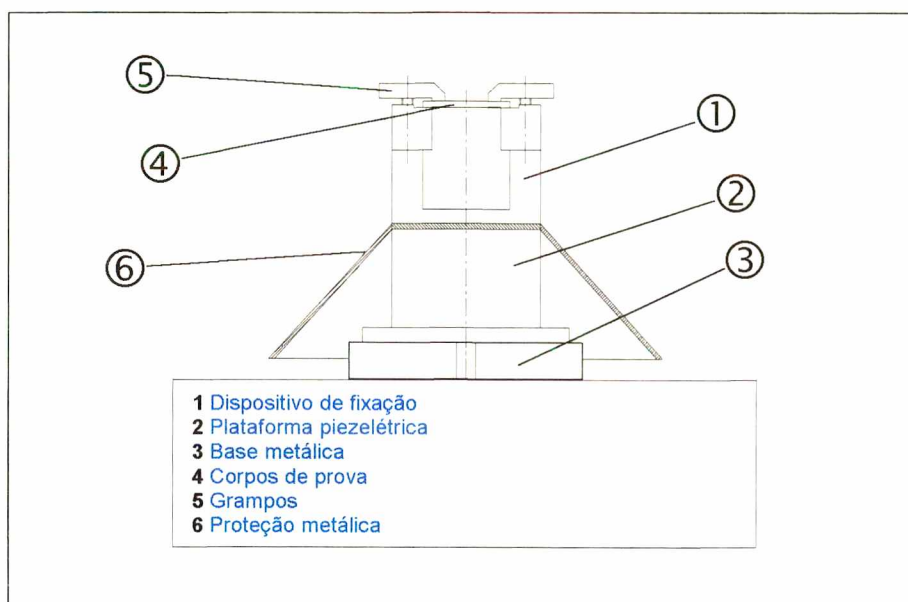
Esquema de montagem do dispositivo de fixação [36].
